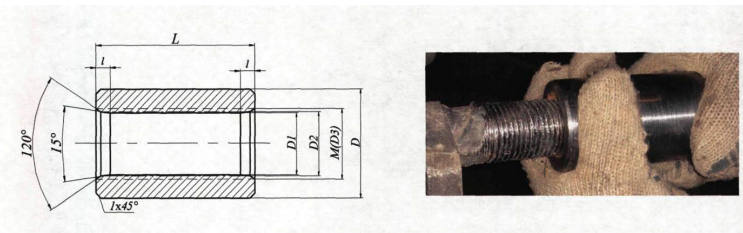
Муфта с цилиндрической накатанной резьбой
